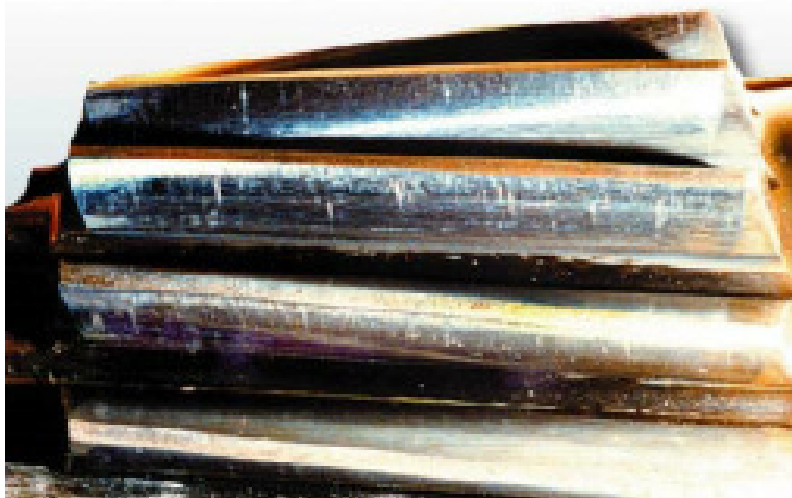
Desgaste adesivo na superfície dos dentes de uma engrenagem [33].
